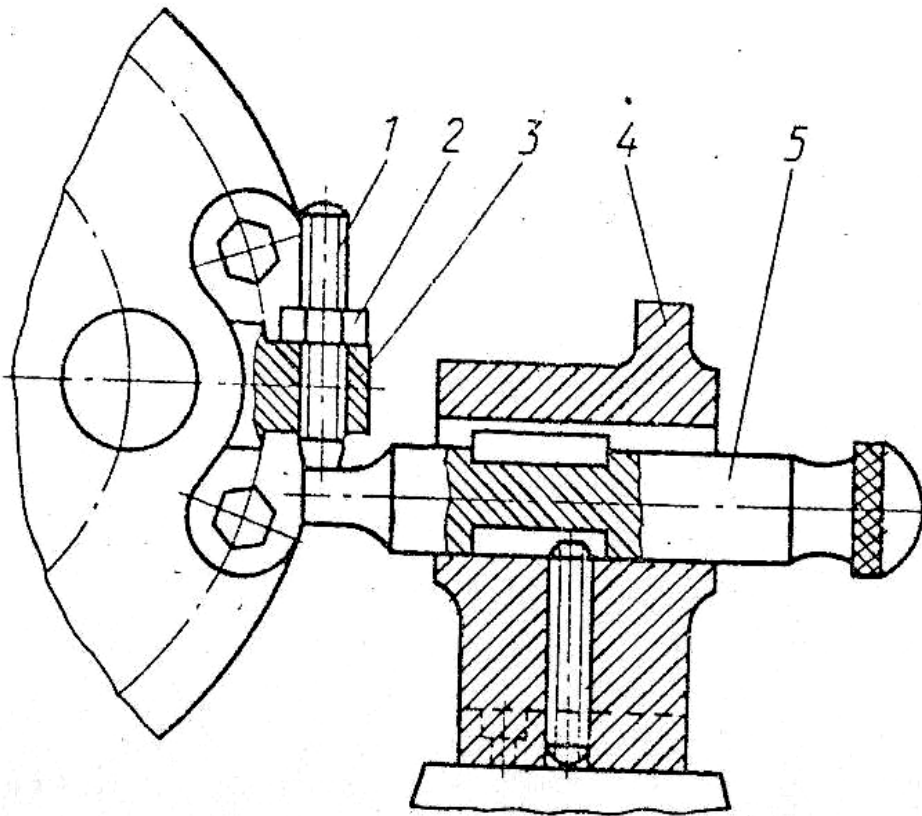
Схема обмежника кругової подачі револьверної головки
